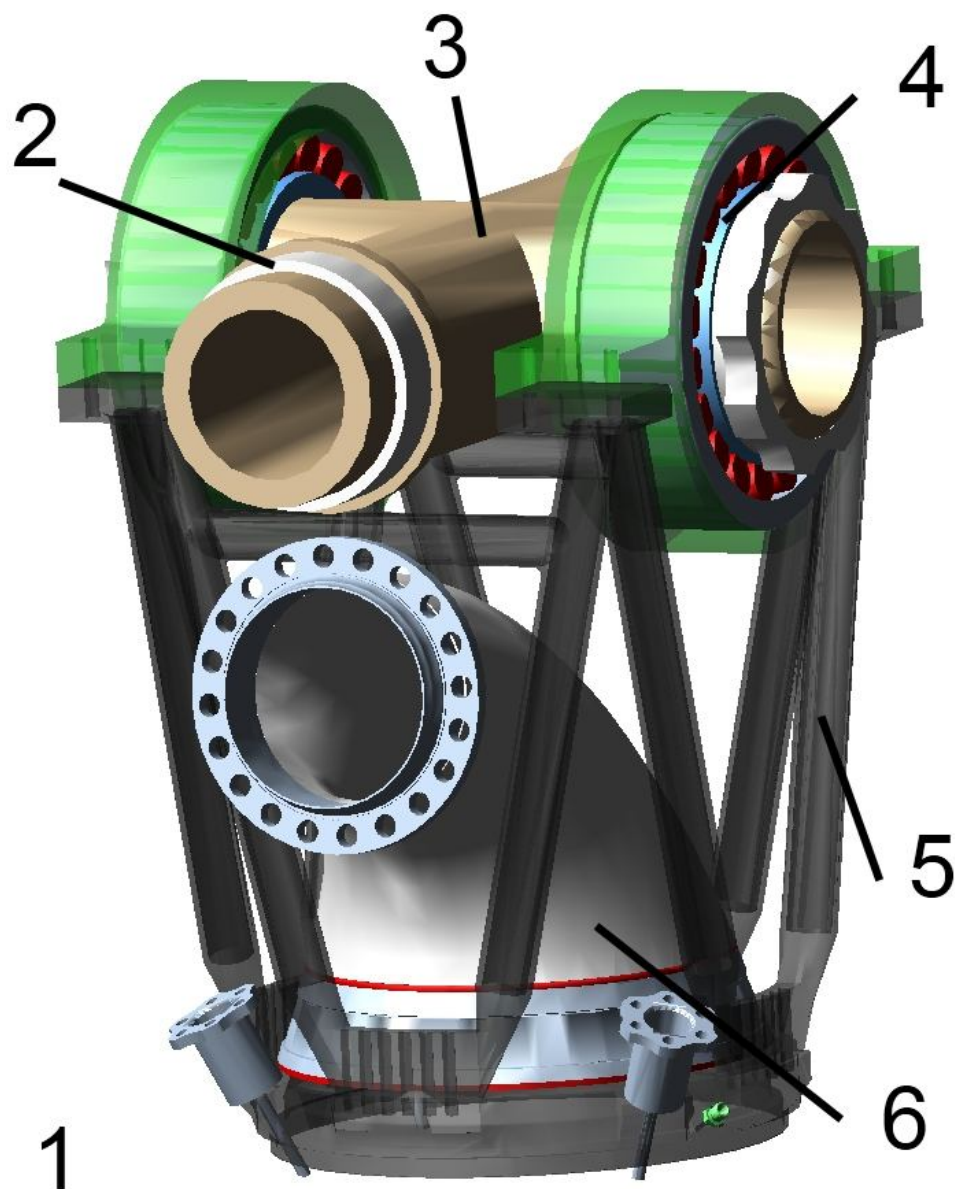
Крепление камеры ЖРД НК-33 в программе ADAMS. Камера в отклонённом положении относительно подвижной оси Кардана (связанной с двигателем): 1 - все поле модели представляет собой Корпус; 2 - подшипники оси Y (скрыты); 3 - крестовина; 4 - подшипники оси X; 5 - рама; 6 - камера.
